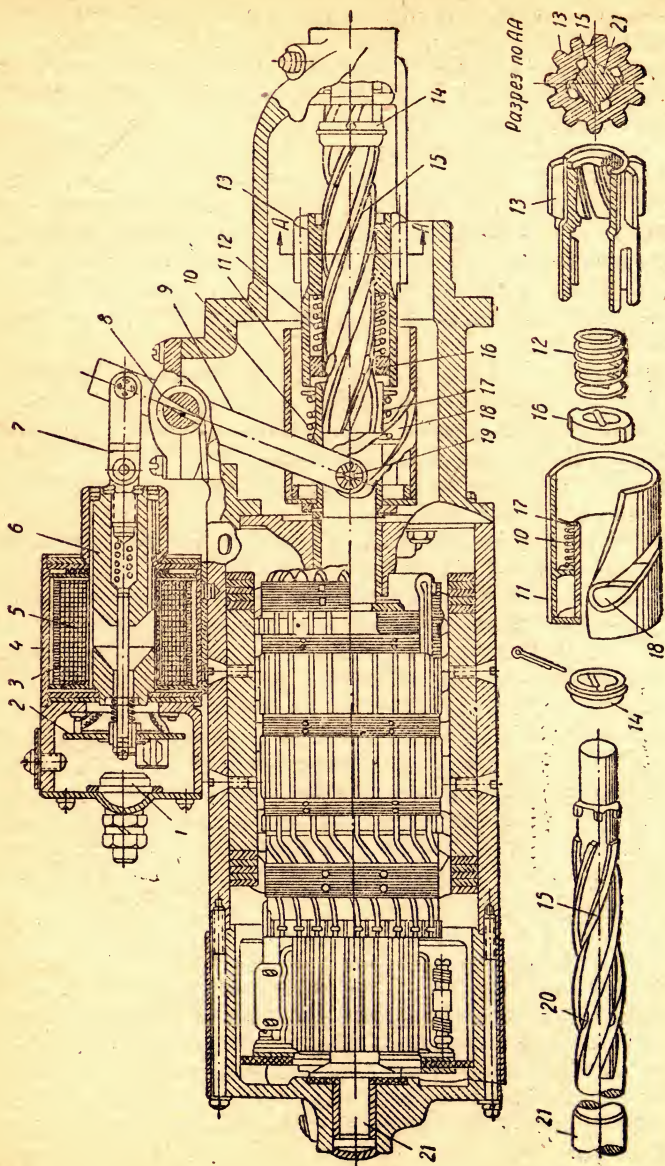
Стартер СТ-103 двигателя ЯМЗ-236
